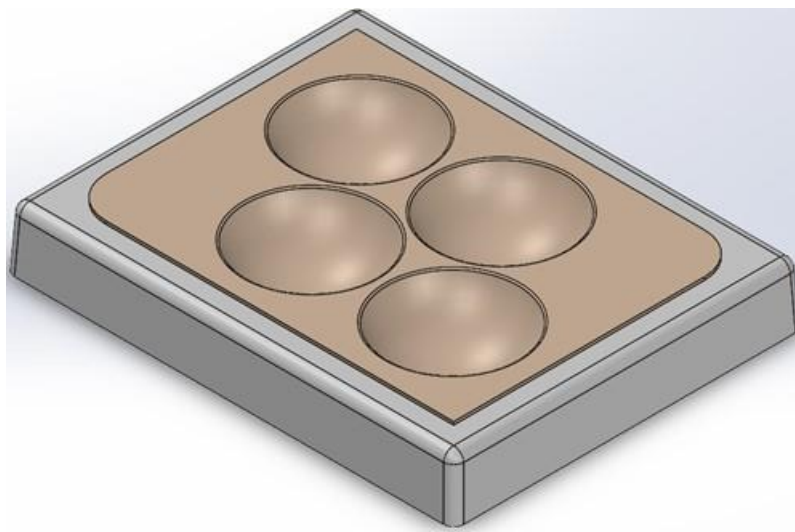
Desenho CAD do molde com a dimensão adequada às folhas produzidas nesta dissertação.
